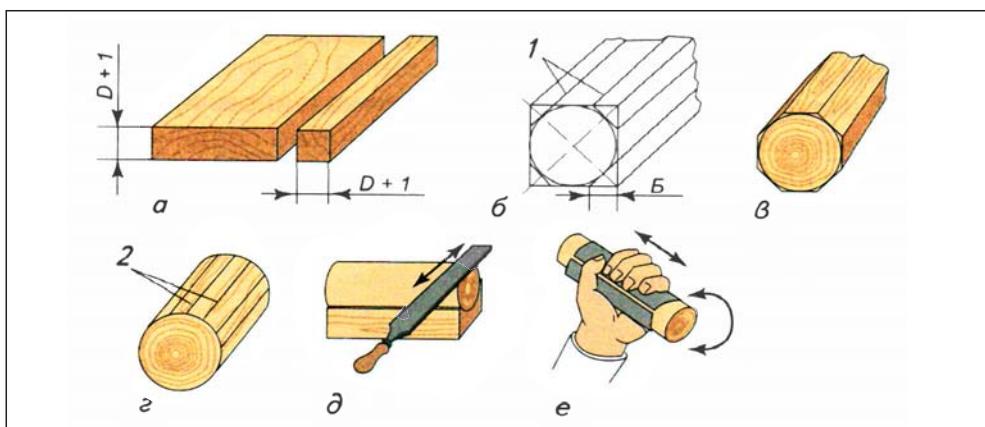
Последовательность изготовления детали цилиндрической формы ручным инструментом:
